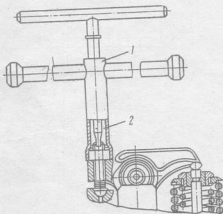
Регулировка тепловых зазоров приспособлением И-801.14.000:
